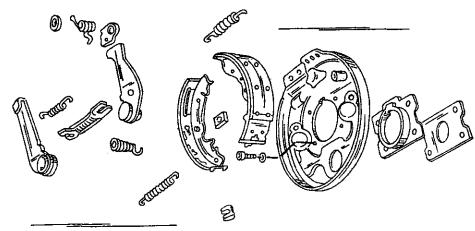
Монтажный чертеж тормоза заднего колеса Bendix.
